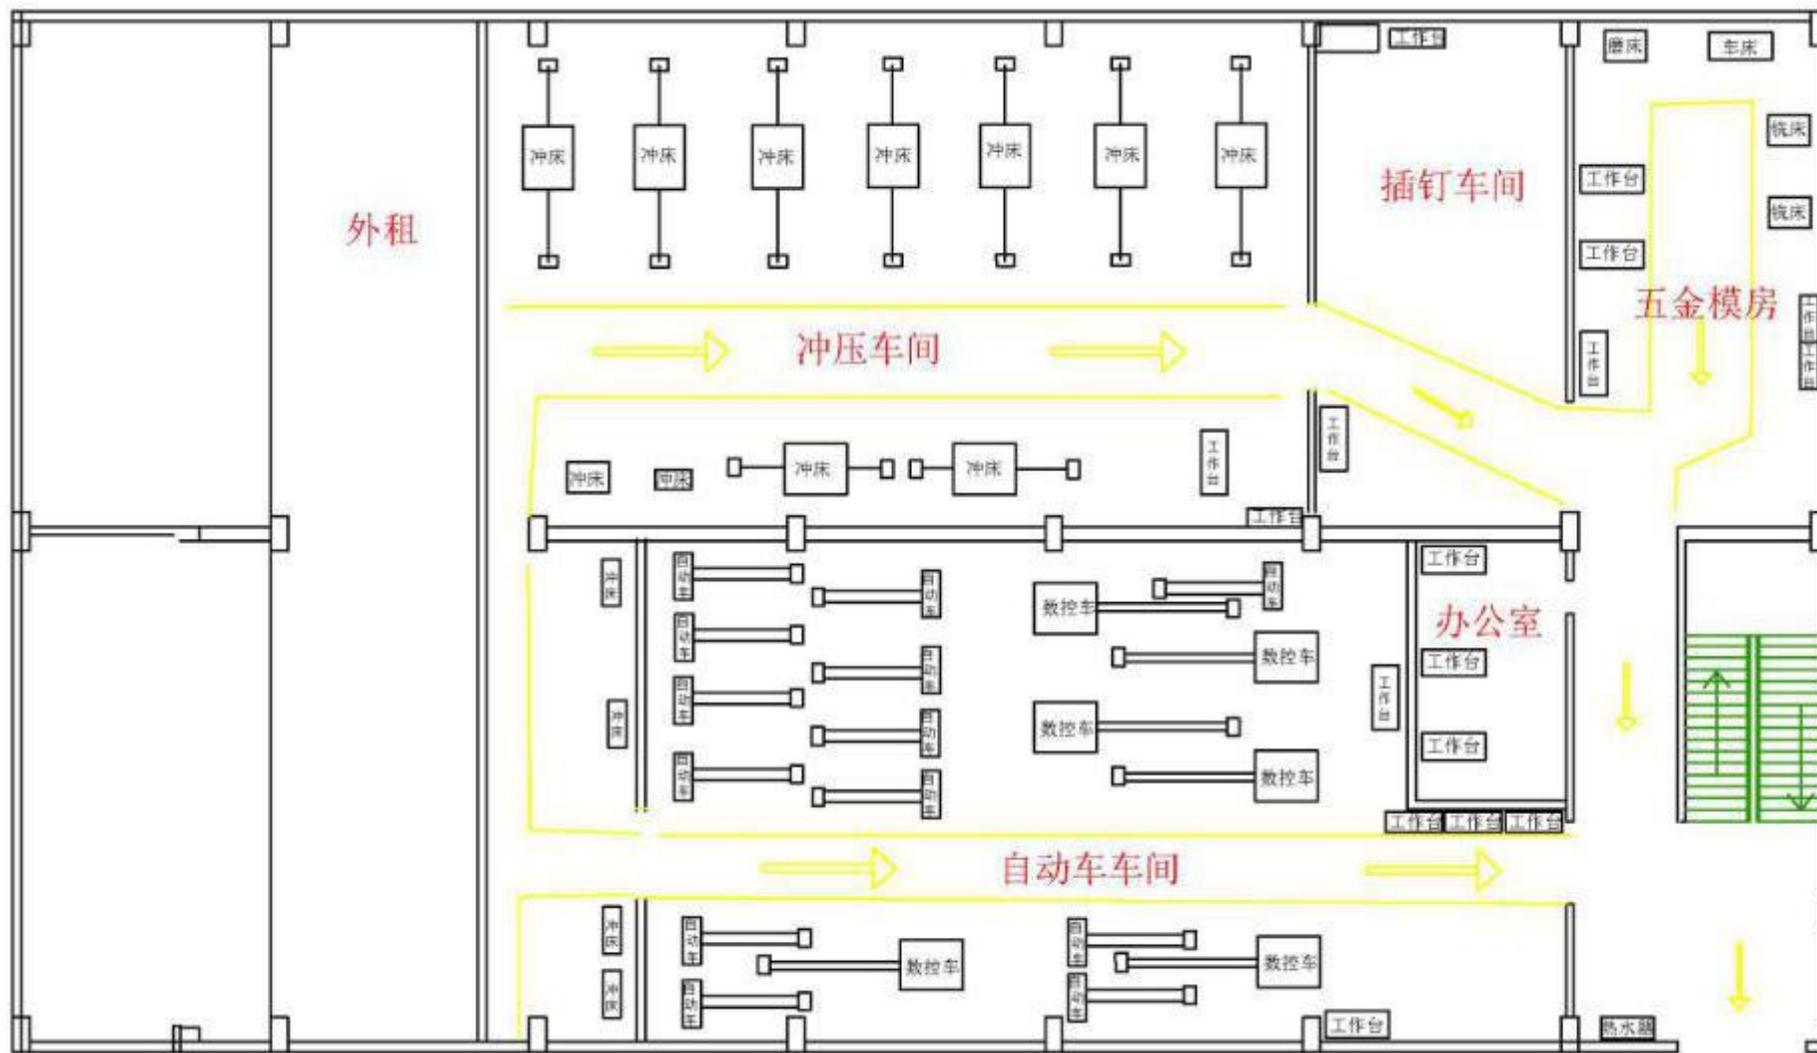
厂房平面布置图（精密五金车间，A栋一层）
